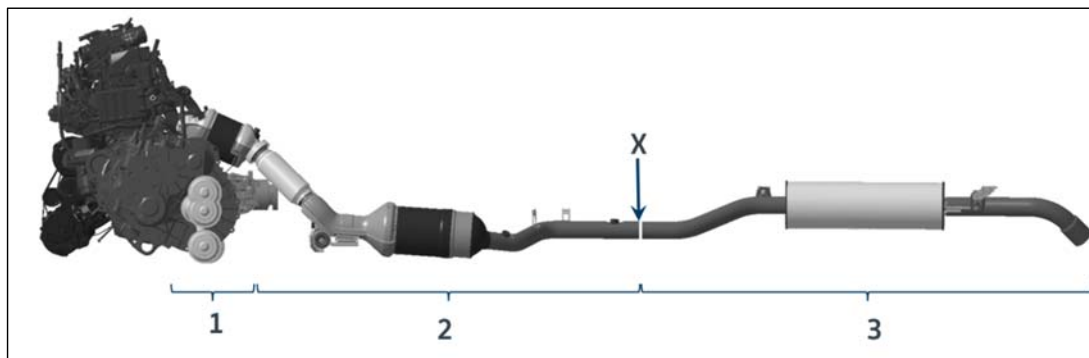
Výfukový systém EU6 se systémem SCR (motor: přední příčné uložení)
